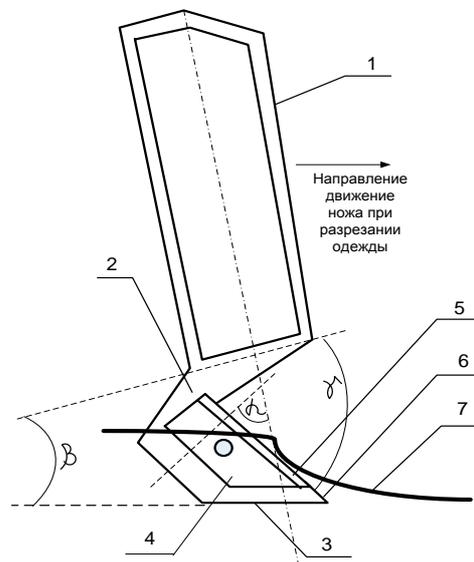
Чертеж ножа 1 – рукоять, 2 – держатель, 3 – торец держателя 4 – лезвие 5 – режущая кромка лезвия 6- кромка, 7 - ткань
